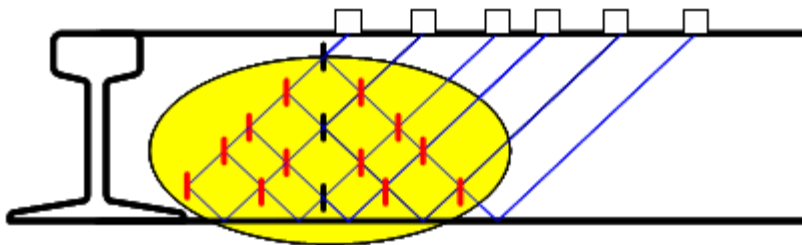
Контроль сварного стыка дефектоскопом МИГ-УКСМ по зеркальному методу
